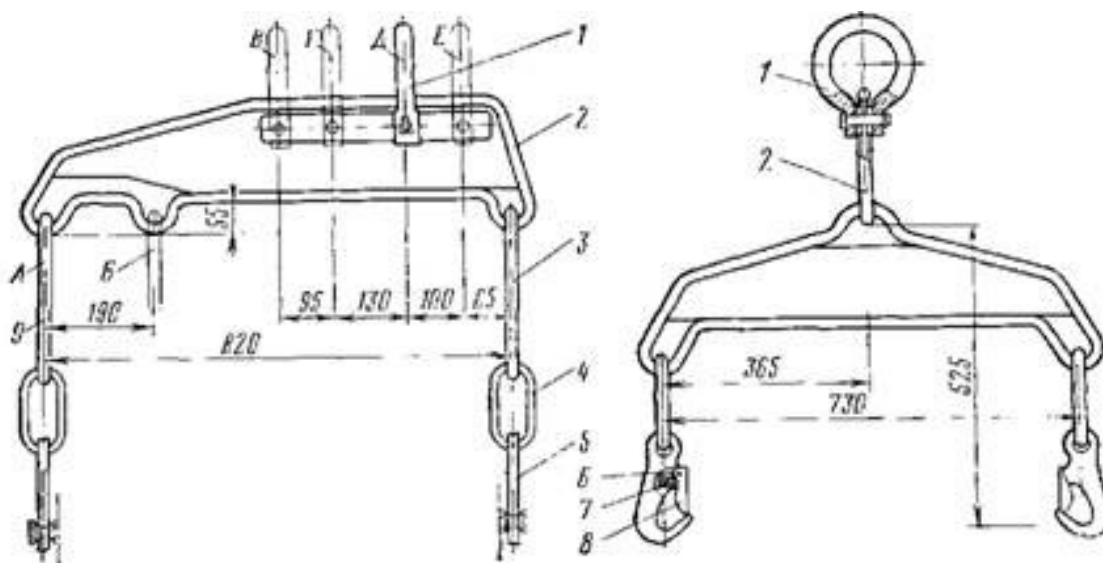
Универсальное приспособление для транспортировки двигателей
